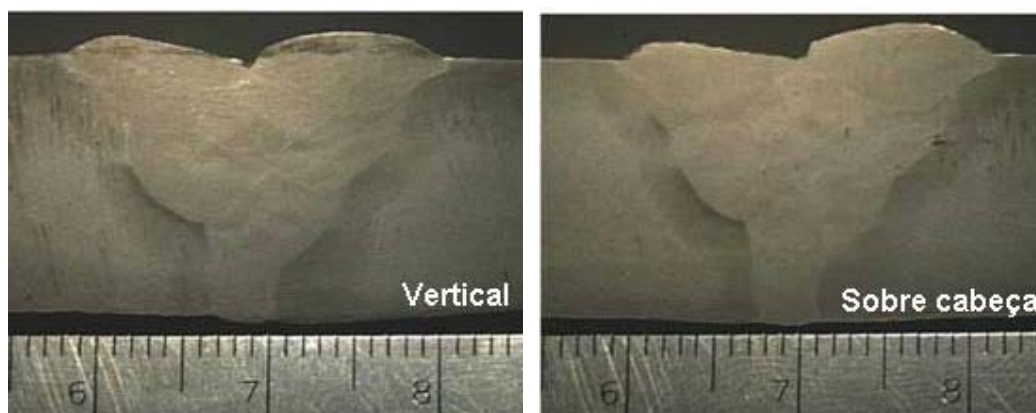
Macrografias de uma solda de um tubo soldado pelo robô na posição 5G.
